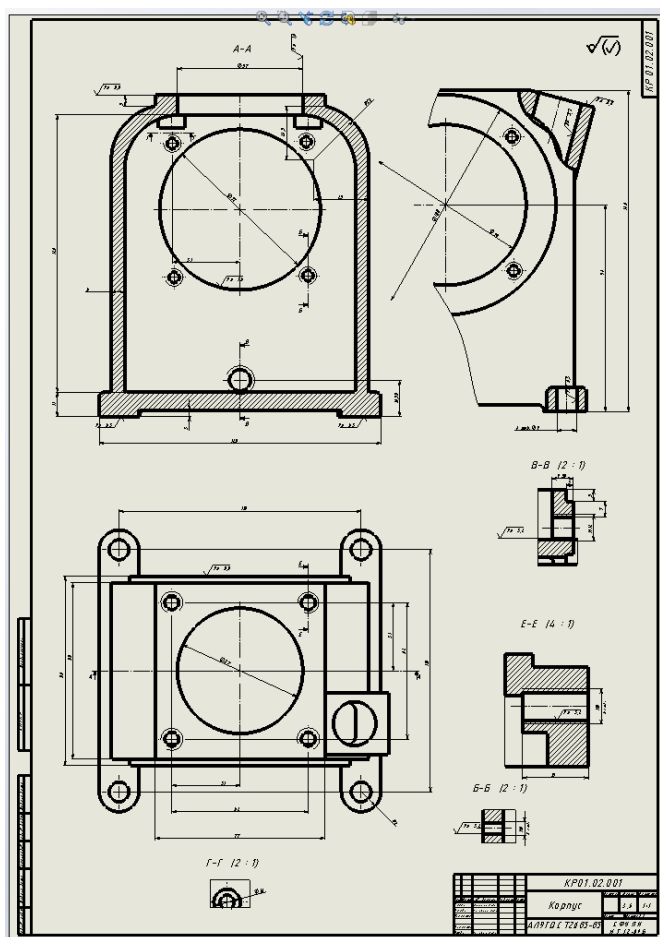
Рабочий чертеж корпуса вакуумного насоса
